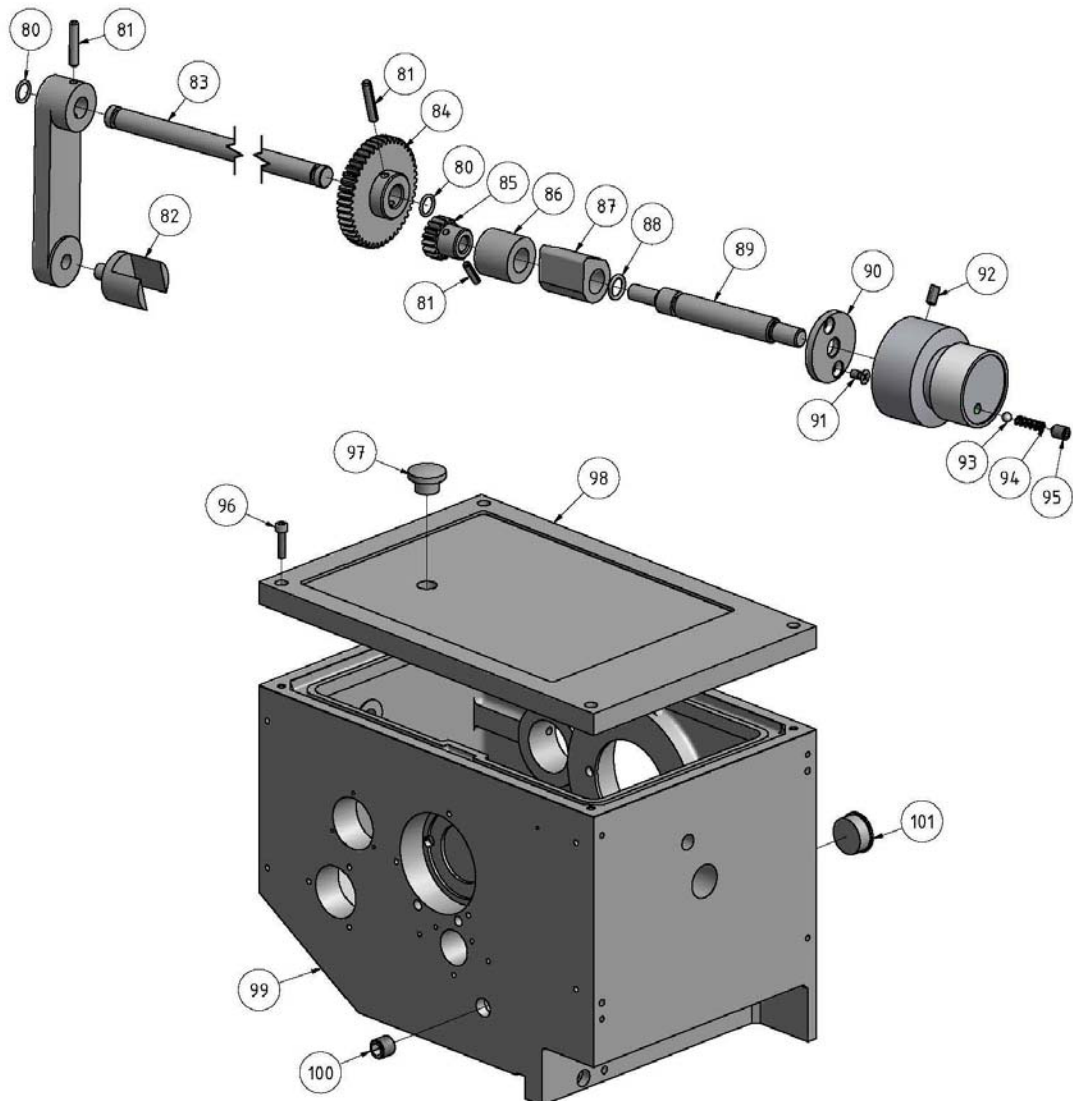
Getriebe Spindelstock 3-3 - Headstock gear 3-3
